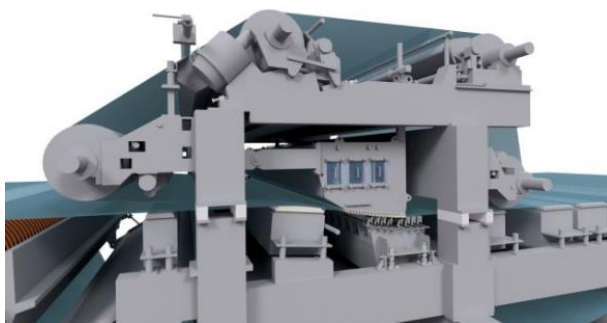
Двосітковий пристрій для формування DuoFormer D II
